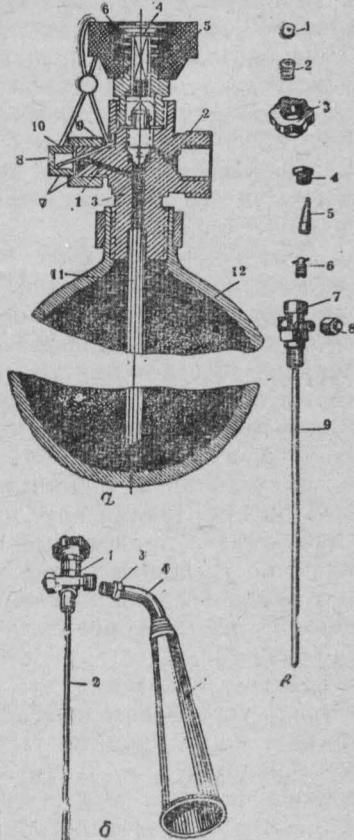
Устройство вентиля углекислотного огнетушителя с поворотным устройством и диффузором:
